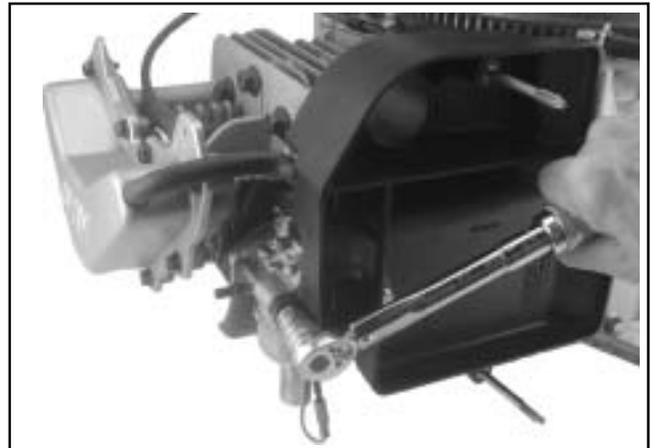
Serraggio dei dispositivi di fissaggio del filtro dell'aria.
